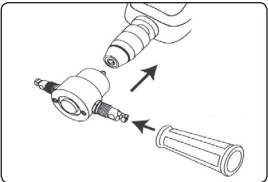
, Montage des Griffs und Befestigung in der Bohrmaschine
